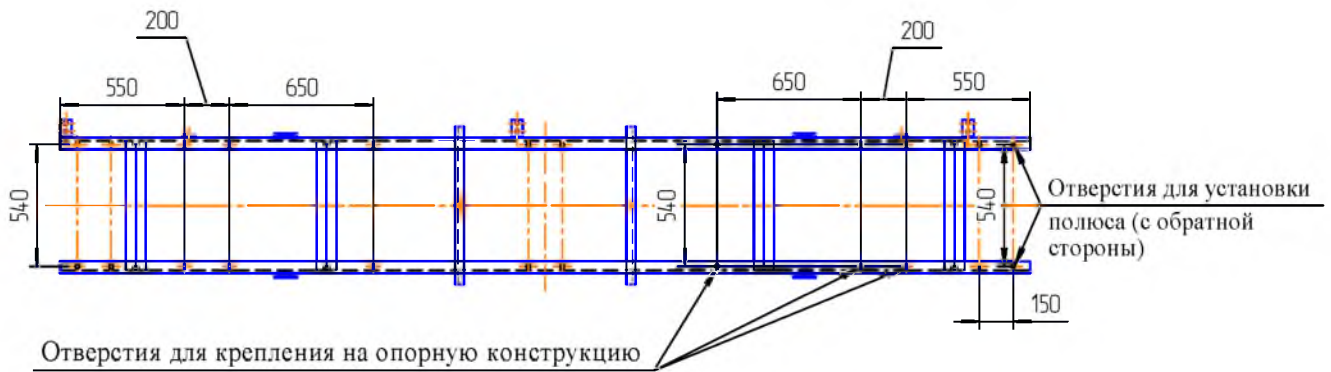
Разметка отверстий на общей раме для крепления ее на опорную конструкцию
